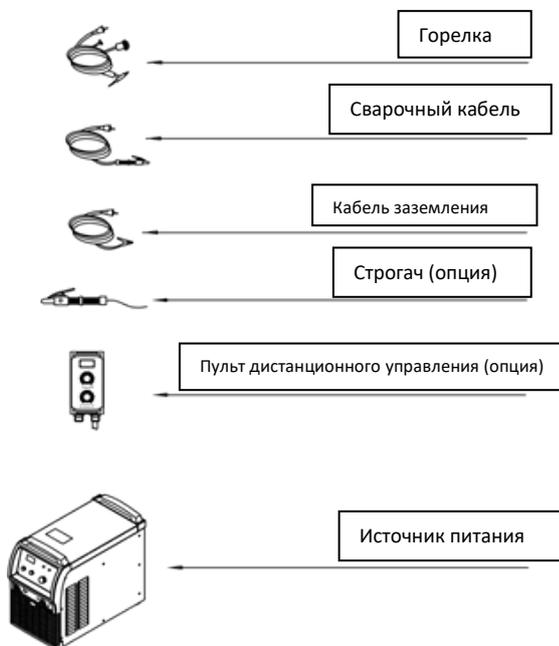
Основные элементы сварочной системы
